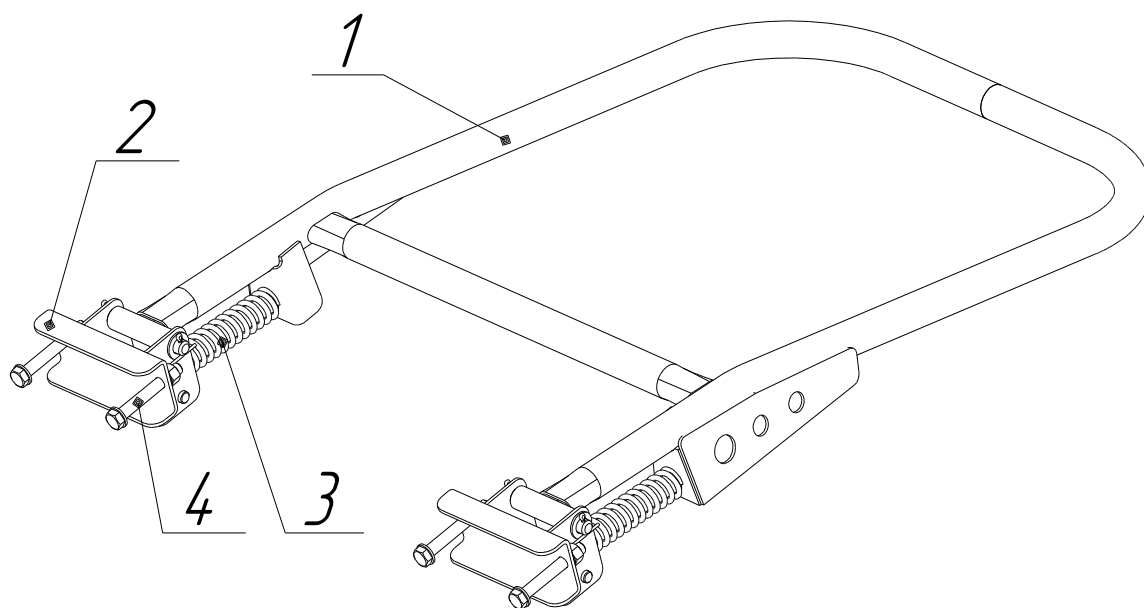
Выбрасыватель рулона: 1- рама; 2 – кронштейн; 3 – пружины; 4 – болты крепления.
